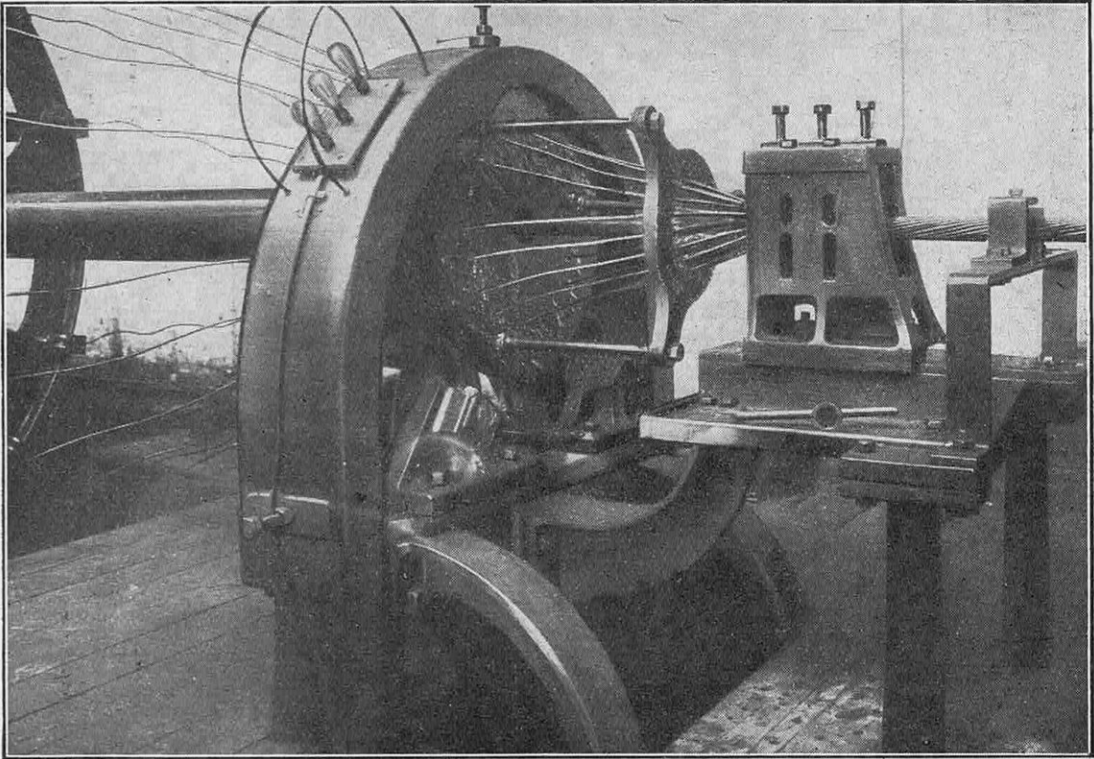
TÊTE DE GROSSE CABLEUSE POUR LA FABRICATION DES CABLES SOUS-MARINS
